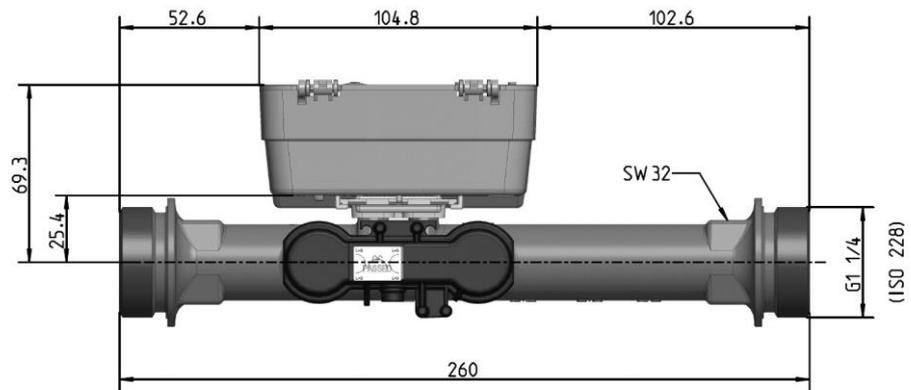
Übersicht Maße Baulänge 260 mm (Gewinde)
